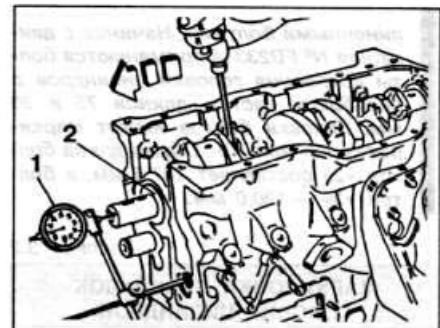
Проверка осевого зазора коленчатого вала:
